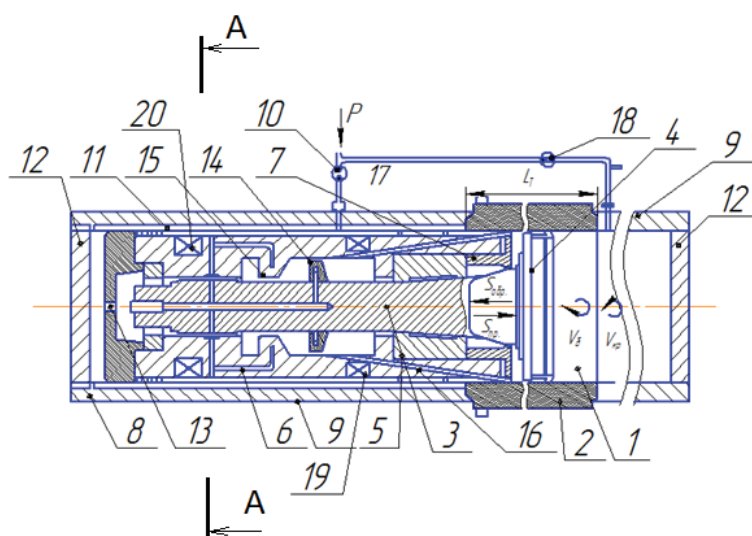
Малогабаритный станок с деформирующим многозубым дорном пиноли для вихрефрезерования глубоких отверстий длинномерных трубных заготовок
